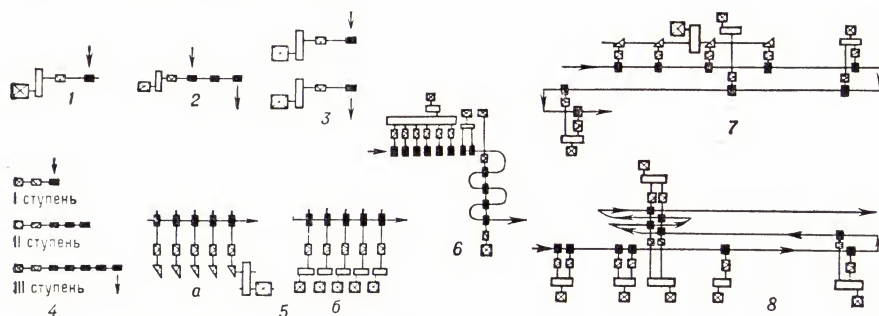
Схемы расположения рабочих клеток прокатного стана: 1 — одноклетевый; 2 — линейный; 3 — двоянный; 4 — ступенчатый; 5 — непрерывного (а — с групповым приводом, б — с индивидуальным); 6 — полунепрерывного; 7 — последовательного («кросс-коунтри»); 8 — шахматного.
